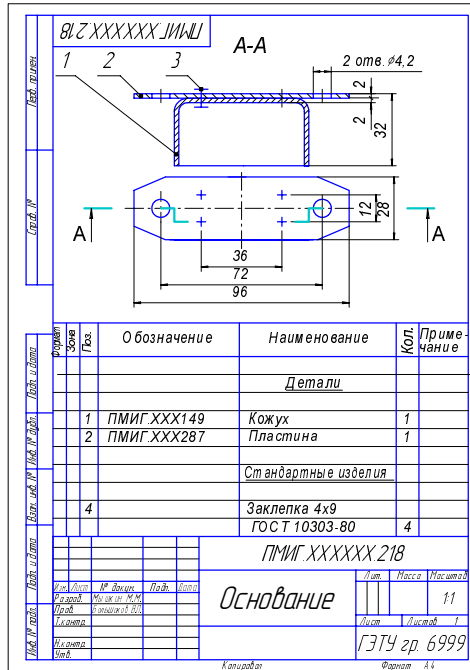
Пример выполнения сборочного чертежа изделия с клепаными соединениями
